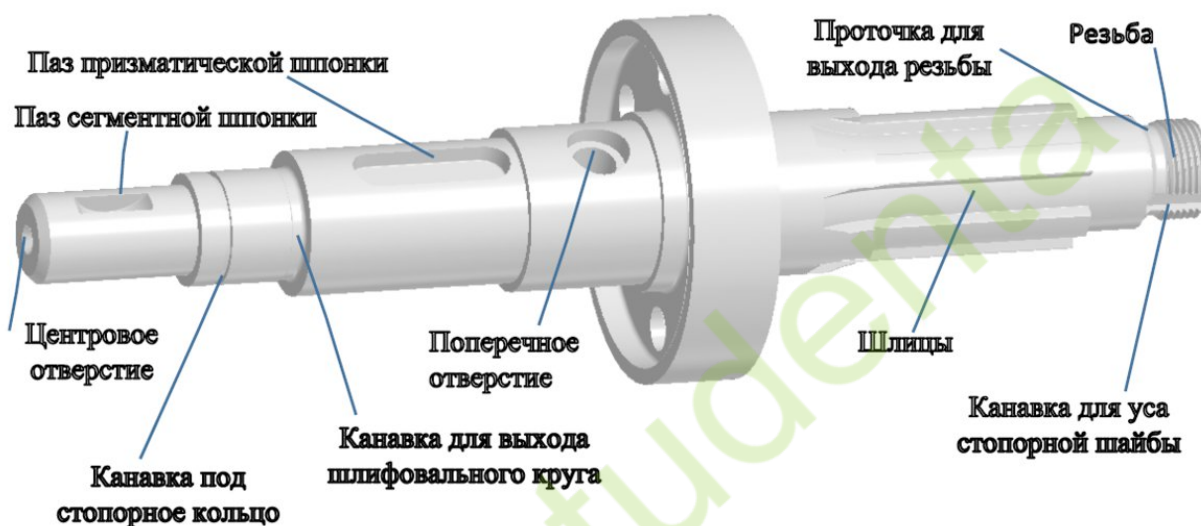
Основные конструктивные элементы детали типа «вал»
